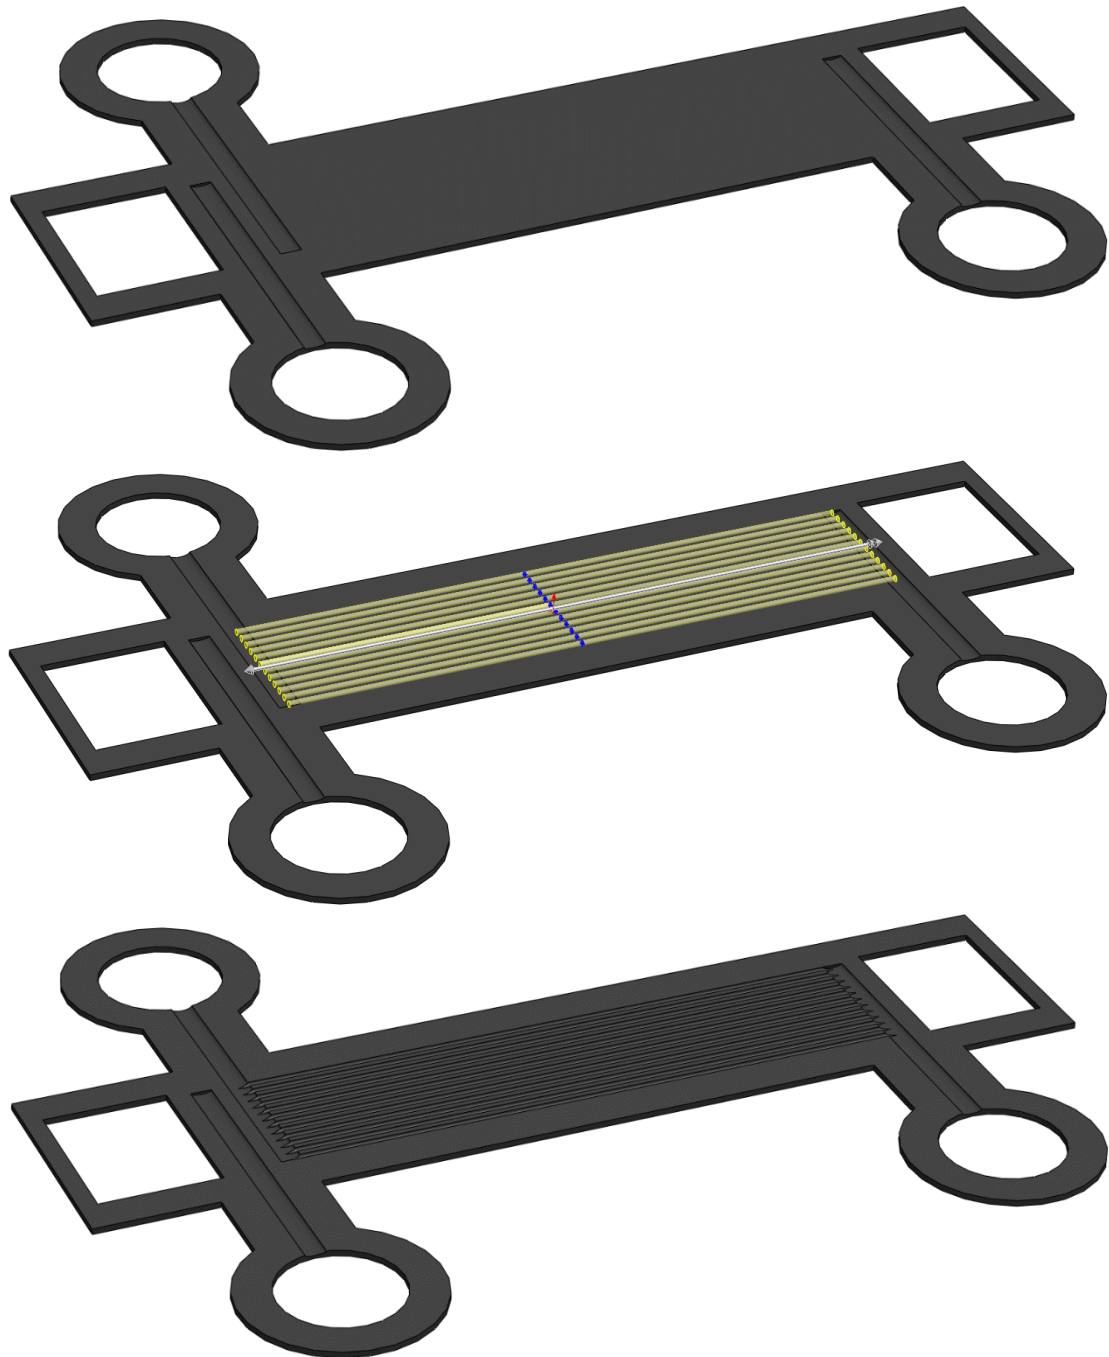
Επιλογές Εντολής Extruded Cut.
